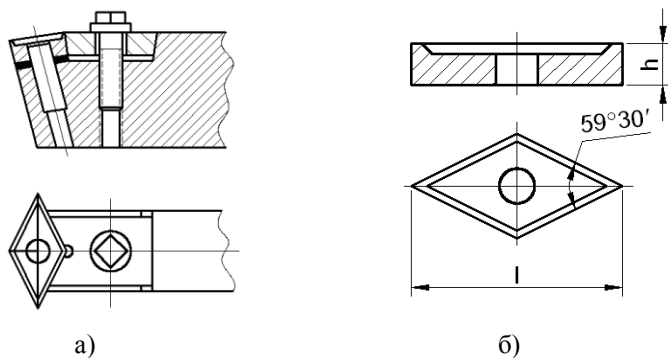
Конструкция ножа (а) с ромбической неперетачиваемой пластиной (б)
